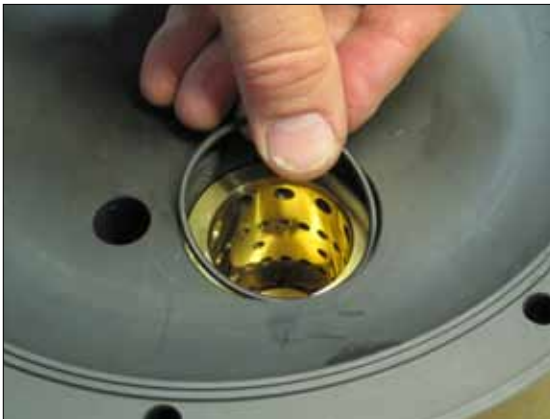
Setzen Sie den letzten O-Ring (30) auf die Hülse.
